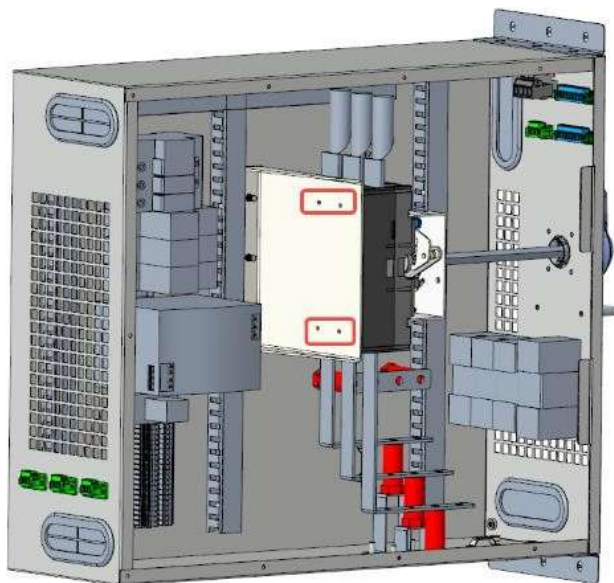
Remova os parafusos de fixação do disjuntor e remova o disjuntor
